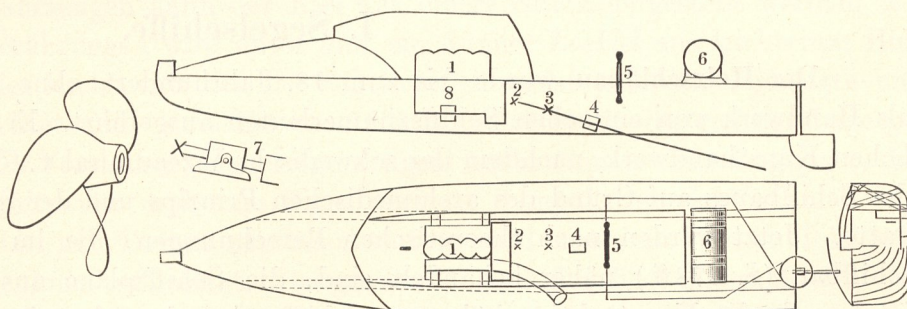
Motorschnellboot „Duc II“ (7,80 m lang, 1,65 m breit; 1 Motor, 2, 3 Kardangelenke, 4 Drucklager, 5 Steuer, 6 Benzintank, 7 Drucklager mit Lafette, 8 Vergaser; Motor 1300 Umdrehungen, Thornycroftschraube [links]).
